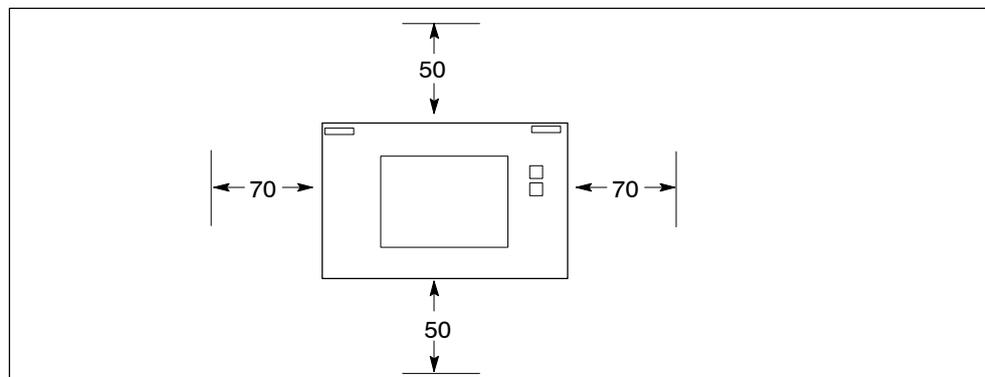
Abstandsmaße beim Einbau des C7-635 Touch
